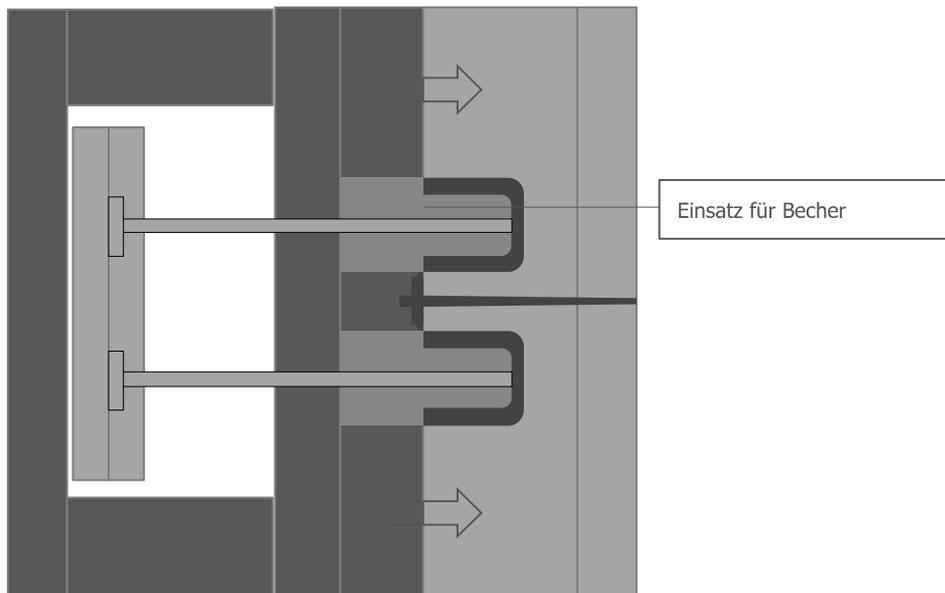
Becherwerkzeug mit Punktanguss – geschlossen
